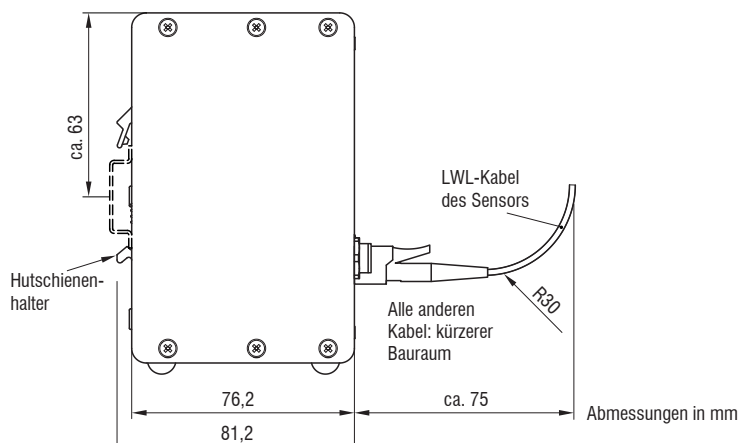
Maßzeichnung Seitenansicht des IMC5200 Controllers
